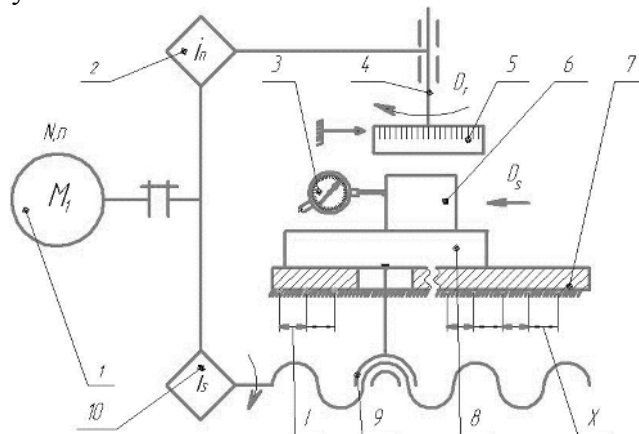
Схема вимірювання величини подачі на зуб фрези:
